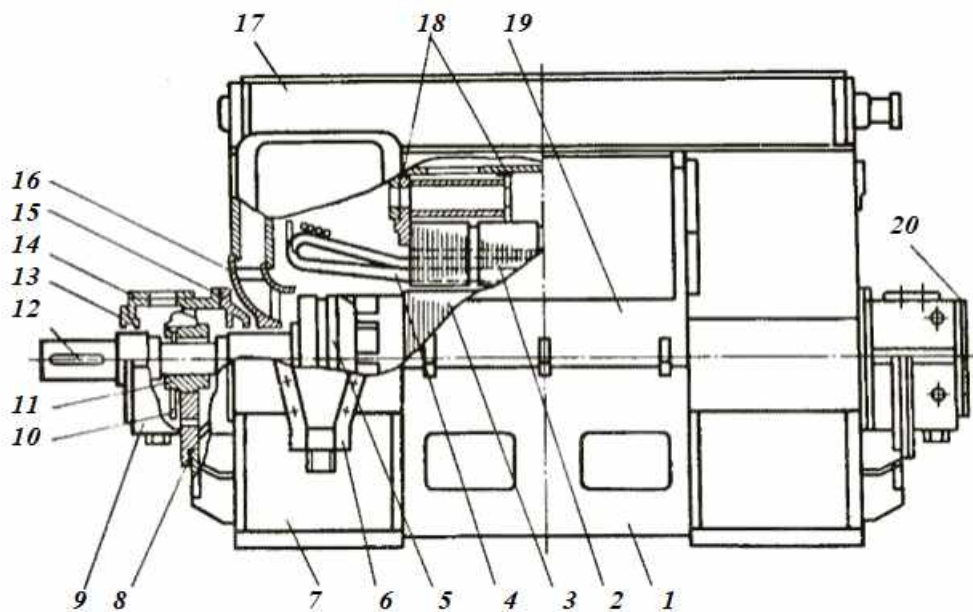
Розріз двигуна 4АЗМ1 - кожух нижній; 2 - сердечник статора; 3 - ротор; 4 - обмотка статора; 5 - вентилятор; 6 - коробка виводів; 7 - щит; 8 - прокладки металеві для регулювання осьового розбігу ротора; 9 - корпус підшипника; 10 - кільце мастильна; 11 - підшипник; 12 - шпонка; 13 - зовнішній масло-збирач; 14 - кришка підшипника; 15 - внутрішній масло-ущільнювач; 16 - щит повітря-спрямовуючий; 17 - повітряохолоджувач; 18 - прокладки ущільнювачів з губчастої гуми; 19 - кожух верхній; 20 - заглушка листів
